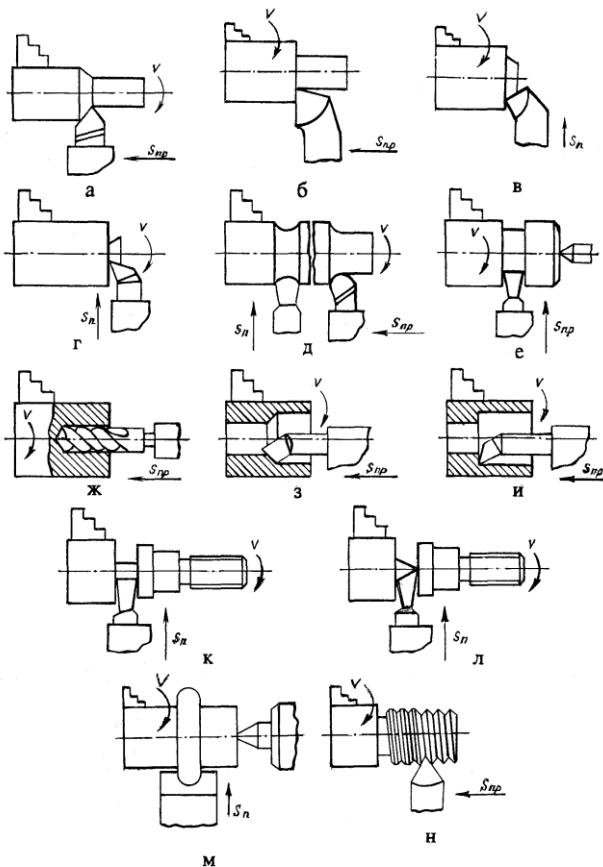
Типы токарных резцов и схемы обработки заготовок на токарных станках: обтачивание наружных цилиндрических поверхностей проходными резцами (*а*) и проходными упорными резцами (*б*); подрезание торцов заготовок подрезными резцами (*в*, *г*); обтачивание скруглений между ступенями валов проходными резцами с закруглениями между режущими кромками или специальными резцами (*д*); протачивание канавок прорезными резцами (*е*); сверление отверстий (*ж*); растачивание внутренних цилиндрических сквозных отверстий проходными резцами (*з*) и ступенчатых и глухих отверстий упорными расточными резцами (*и*); отрезка обработанных деталей отрезными резцами с прямой главной режущей кромкой (*к*) и с наклонной режущей кромкой (*л*); обработка фасонных поверхностей фасонными резцами (*м*); обработка наружных резьб резьбовыми резцами (*н*)
